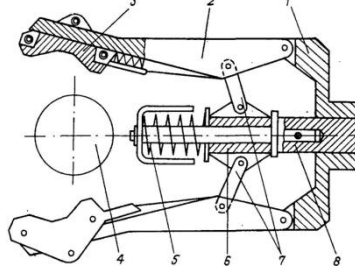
Схема захватного пристрою з обертальним рухом губок другого типу
